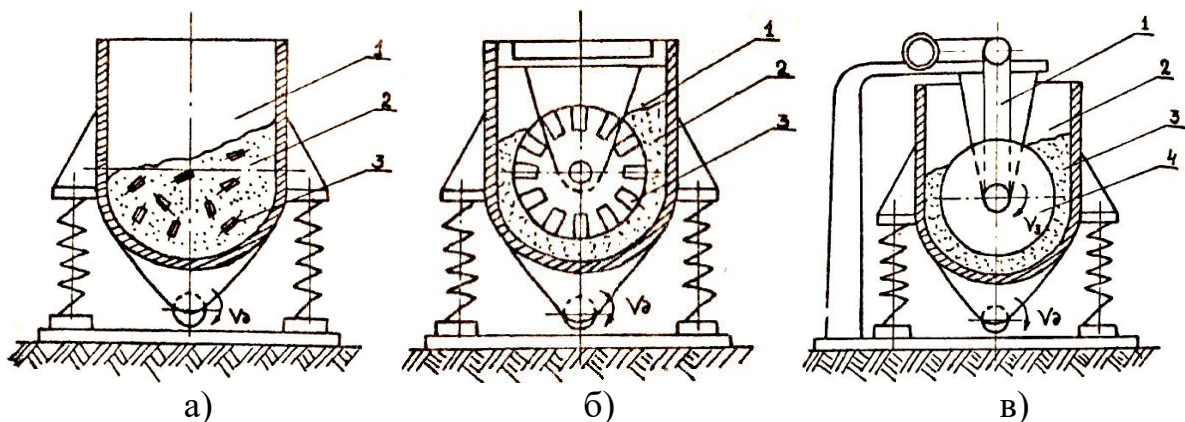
Схема відроабразивної обробки без закріплення заготовок (а), із закріпленням і вільним обертанням заготовок (б) та із закріпленням і примусовим обертанням заготовок (в): 1 – камера V-подібного контейнера, 2 – абразивний наповнювач, 3 – оброблювана заготовка, V_d – частота обертання вала з дисбалансом, V_z – частота обертання заготовки
